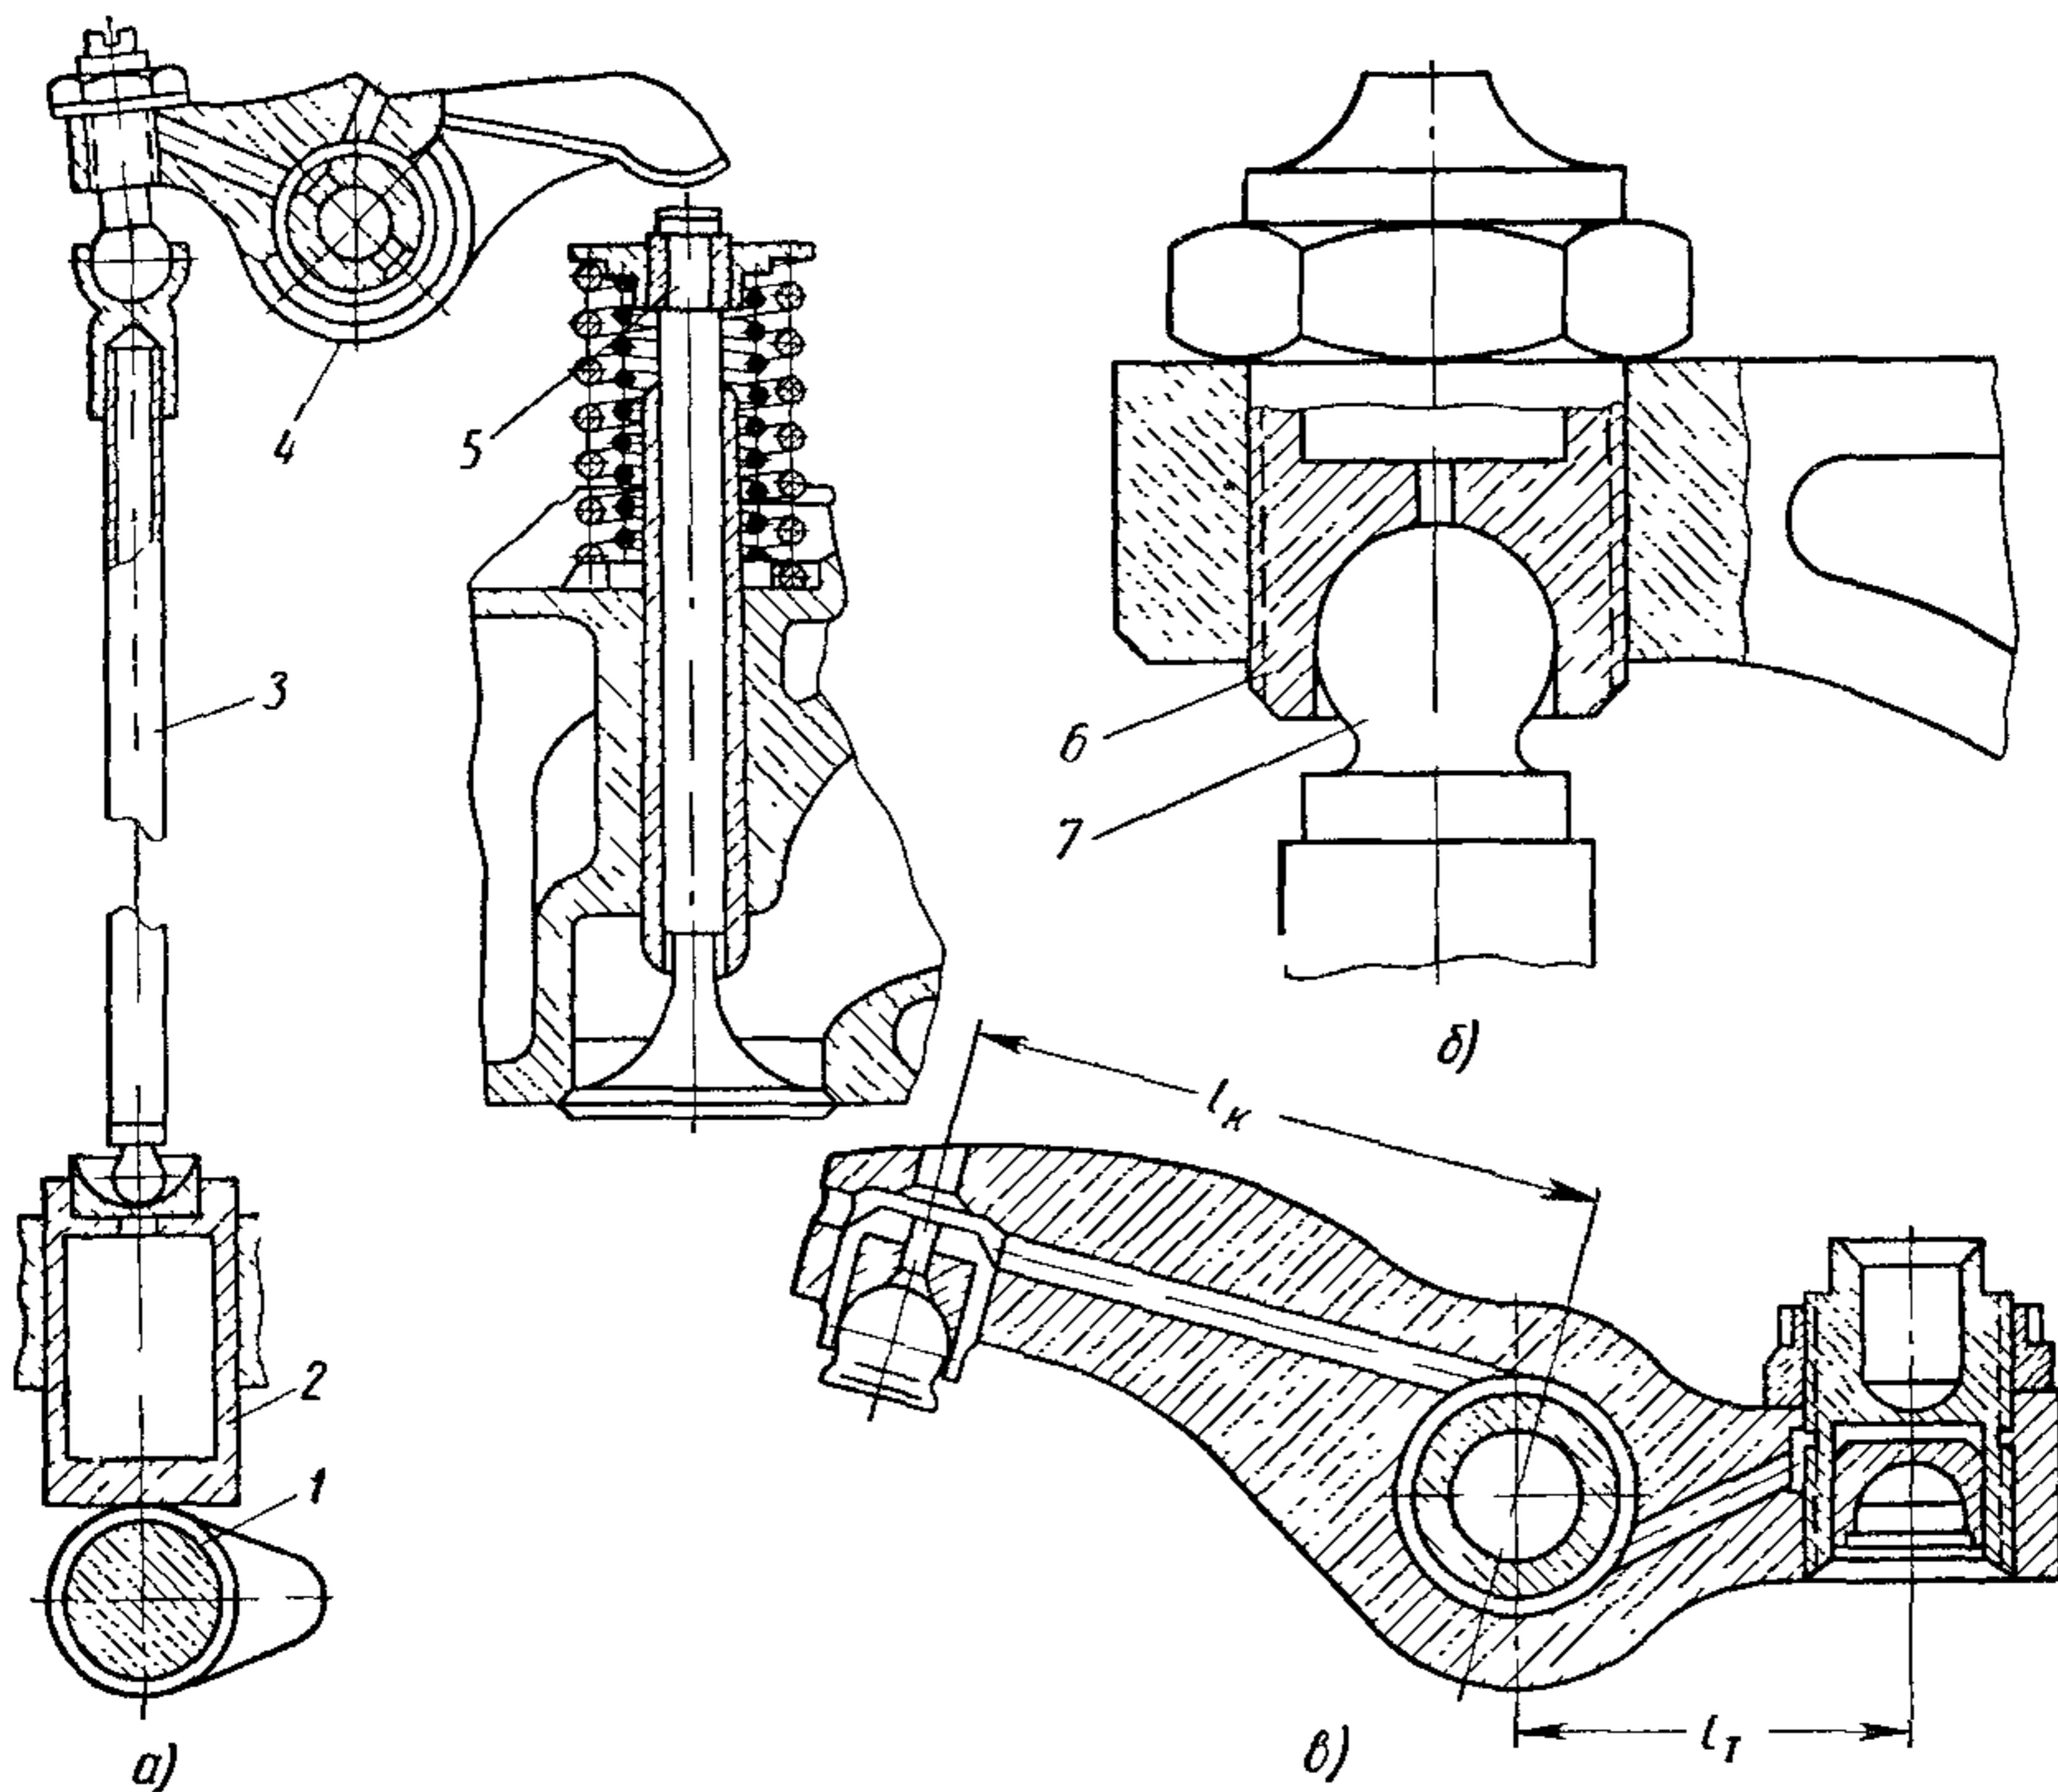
Детали передаточного механизма при верхнем расположении клапанов
